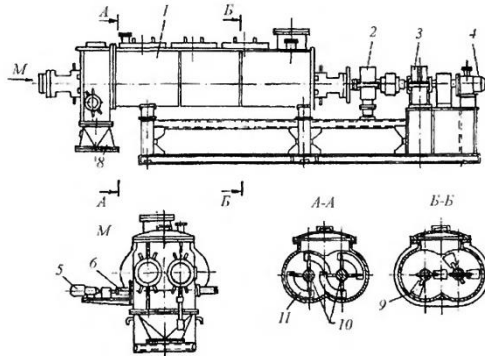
17 – Загальний вигляд безперервної дії змішувача з нерухомим корпусом: 1 – корпус; 2 – зубчасті пари; 3 – редуктор; 4 – електродвигун; 5 – привід розпушувача; 6 – розпушувач; 7 – рама; 8 – завантажувальна камера; 9 – лопатки; 10 – вали; 11 – спіральні стрічки
